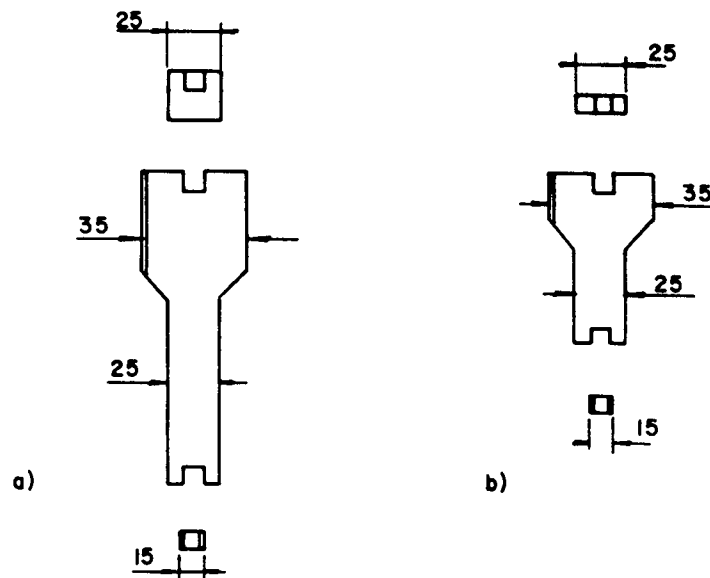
Vista explodida da parte lateral dos quadros.
